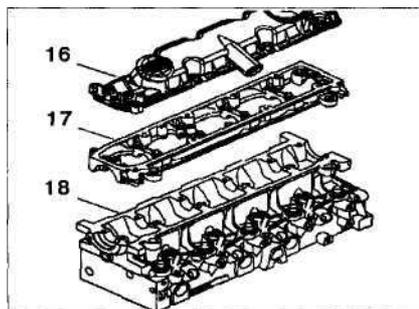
Крышка головки блока цилиндров 16, головка блока цилиндров 18 и корпус распределительного вала 17.
